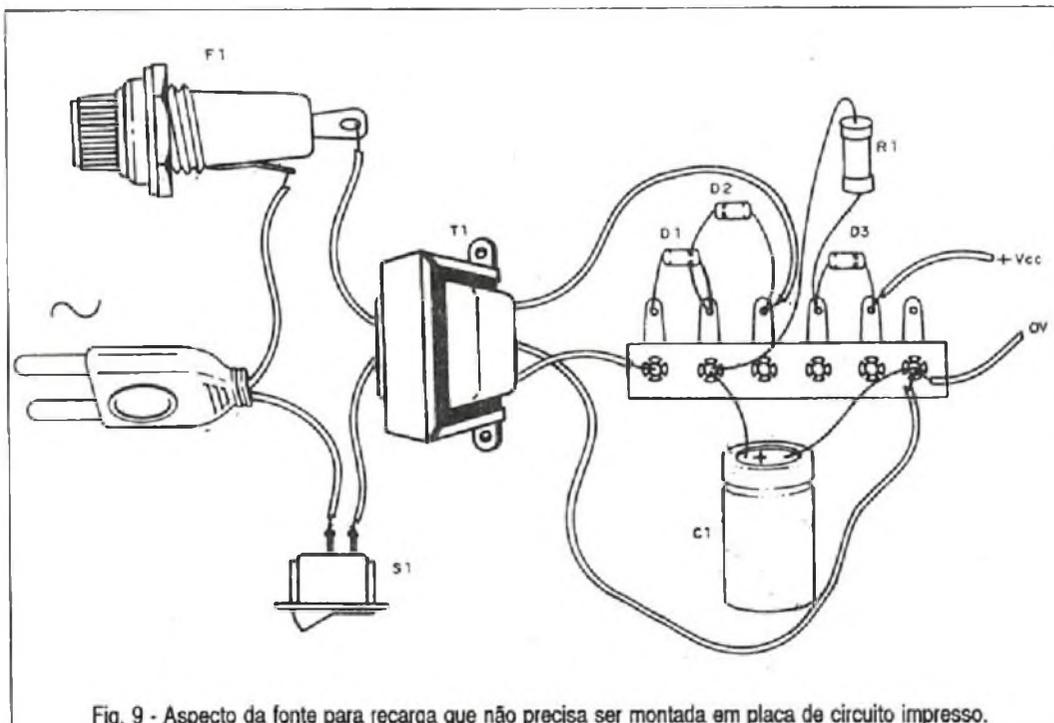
Aspecto da fonte para recarga que não precisa ser montada em placa de circuito impresso.
